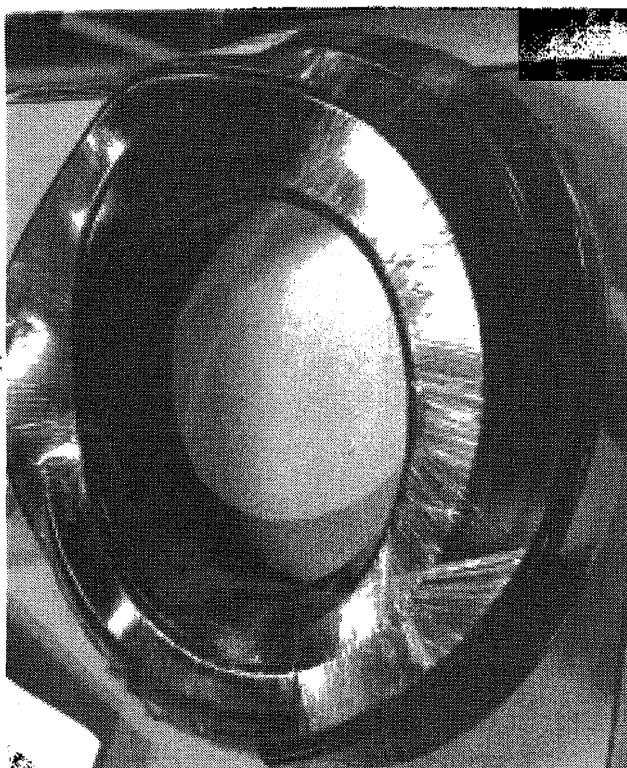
Защитный кожух главного кабеля напольного автозагрузчика
